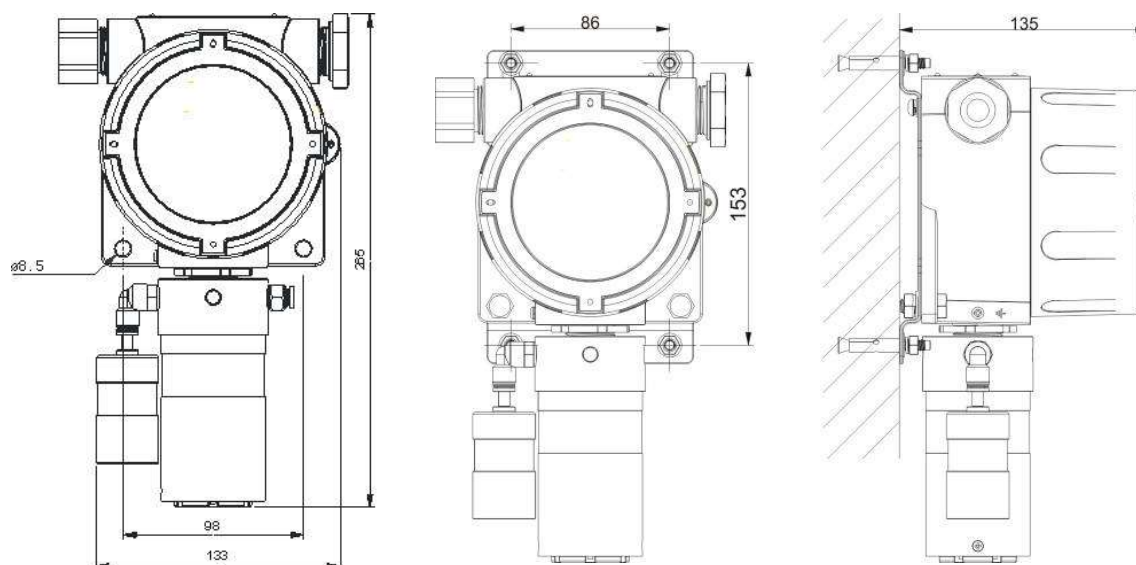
Габаритные и установочные размеры газоанализатора ЭССА-М-ИП, Ф-ИВНО
